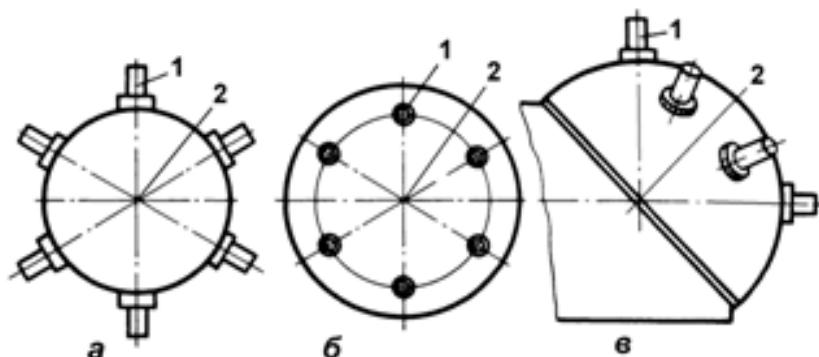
Інструментальні магазини с інструментом, закріпленим в шпиндельних вузлах
